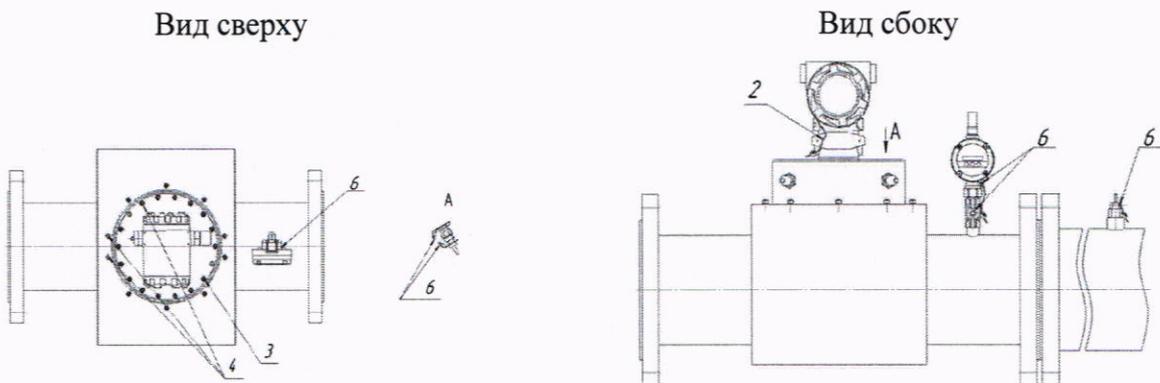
Корпус круглого сечения с защитным кожухом
